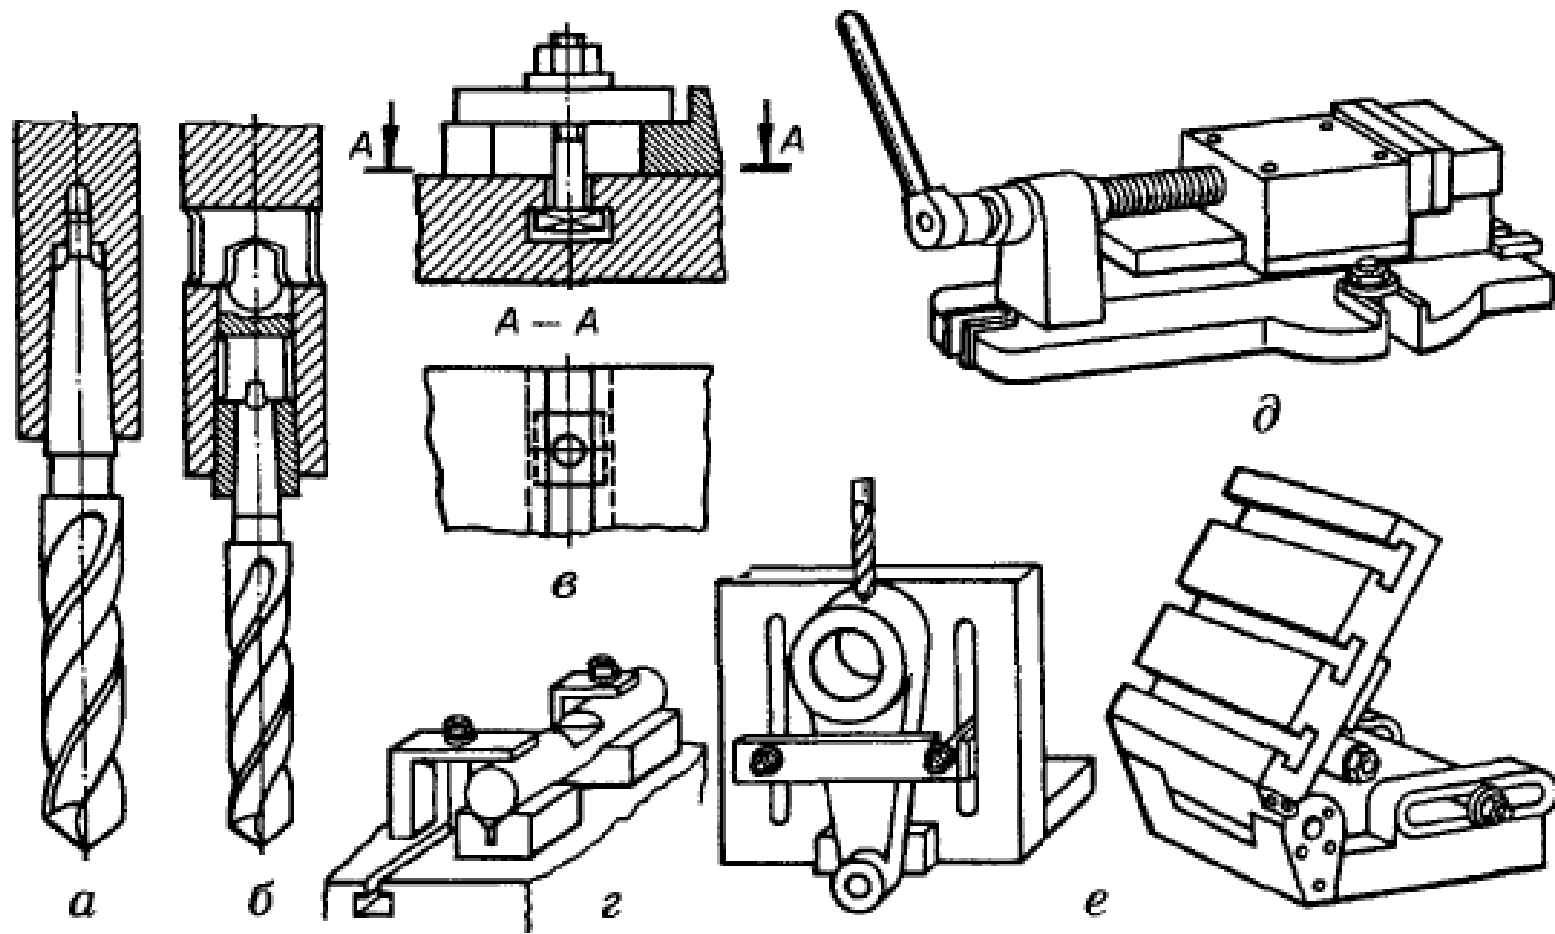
Кріплення інструмента і заготовок на свердильних верстатах
